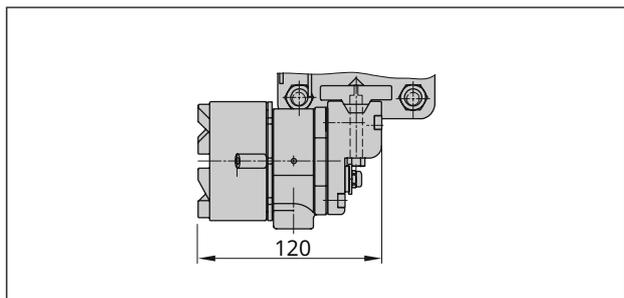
Размеры в мм · Тип 6116-xx06011x000xxxx без усилителя согласно NAMUR для Tuna 4765/3760
